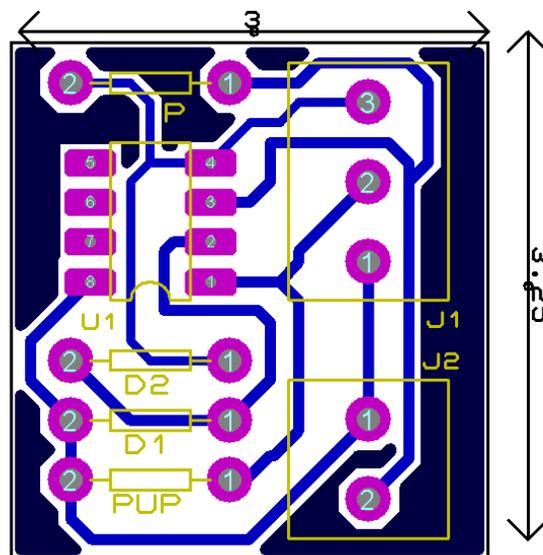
“Diseño de PCB circuito de monitoreo de luz”
